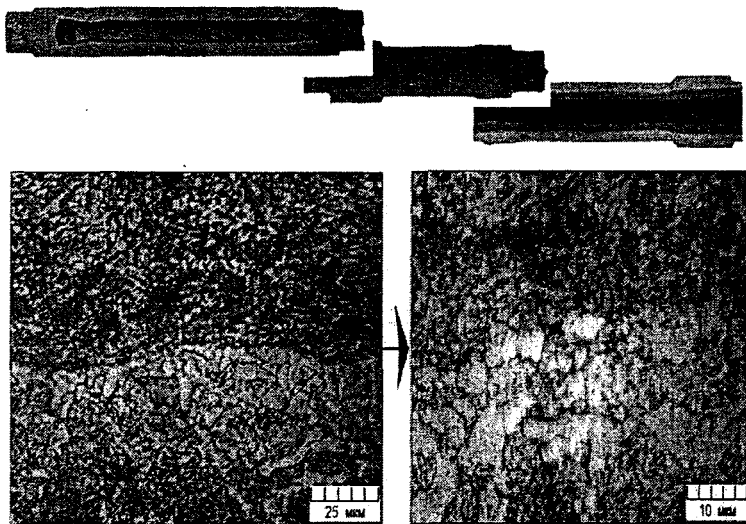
Сварные слоистые детали из однородных и разнородных сталей
